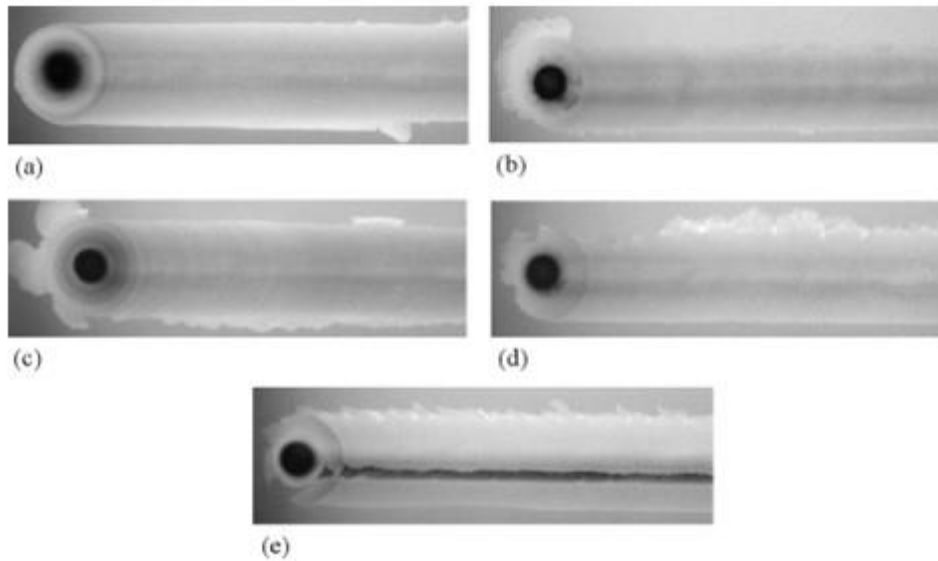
Radiografías de uniones realizadas por FSW a diferentes velocidades. (a) 50 mm/min; (b) 100 mm/min; (c) 150 mm/min; (d) 200 mm/min; (e) 250 mm/min. (43)
